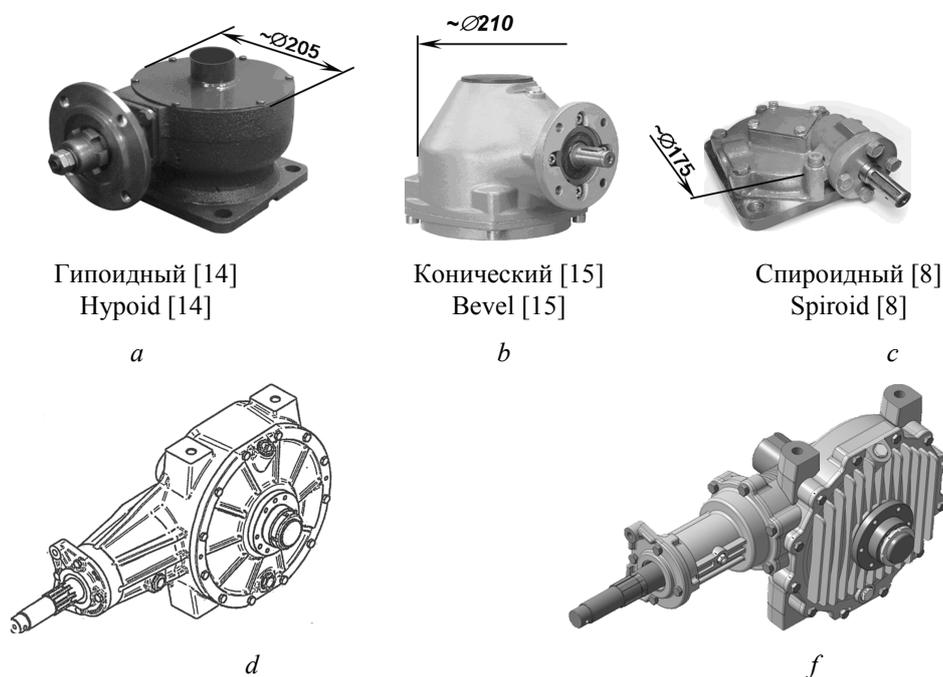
Примеры спиридных редукторов взамен конических и гипоидных: а-с – редукторы ТПА с нагрузочным моментом 1000 Нм; d, f – редукторы прессподборщика
